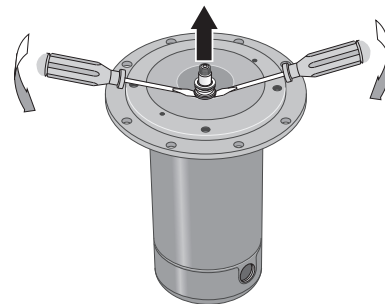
RETIRE LA PLACA DE LA JUNTA
